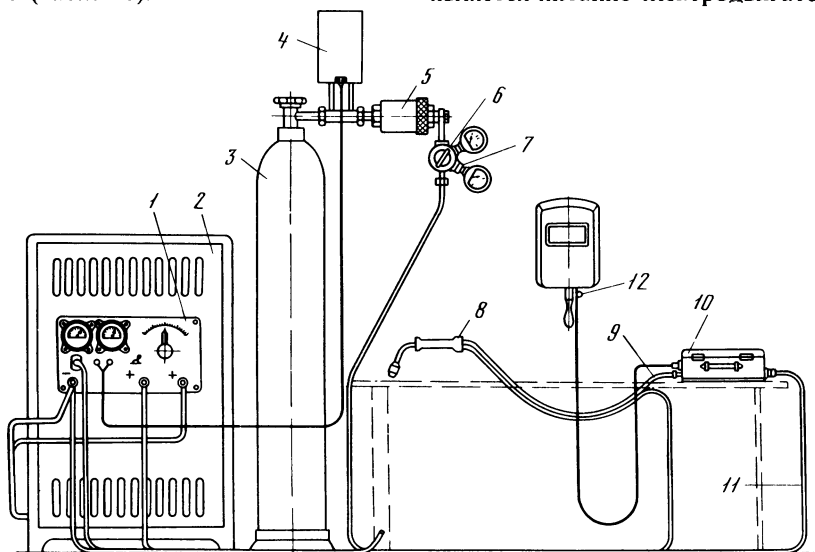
Полуавтомат А-547У для сварки в газе:
